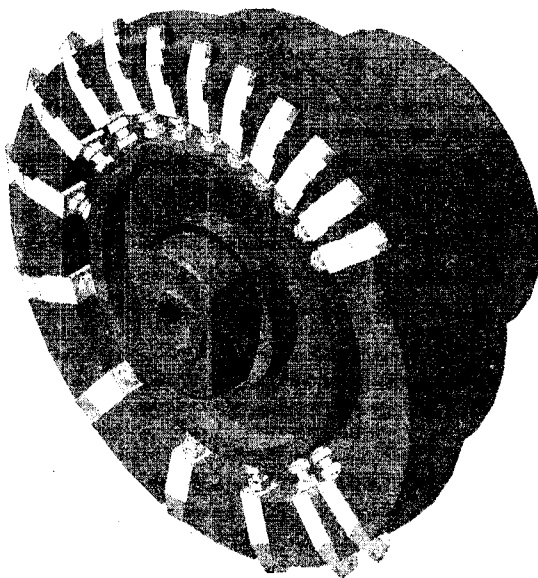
Общий вид резцовой головки для обкатывающего зубопротягивания
